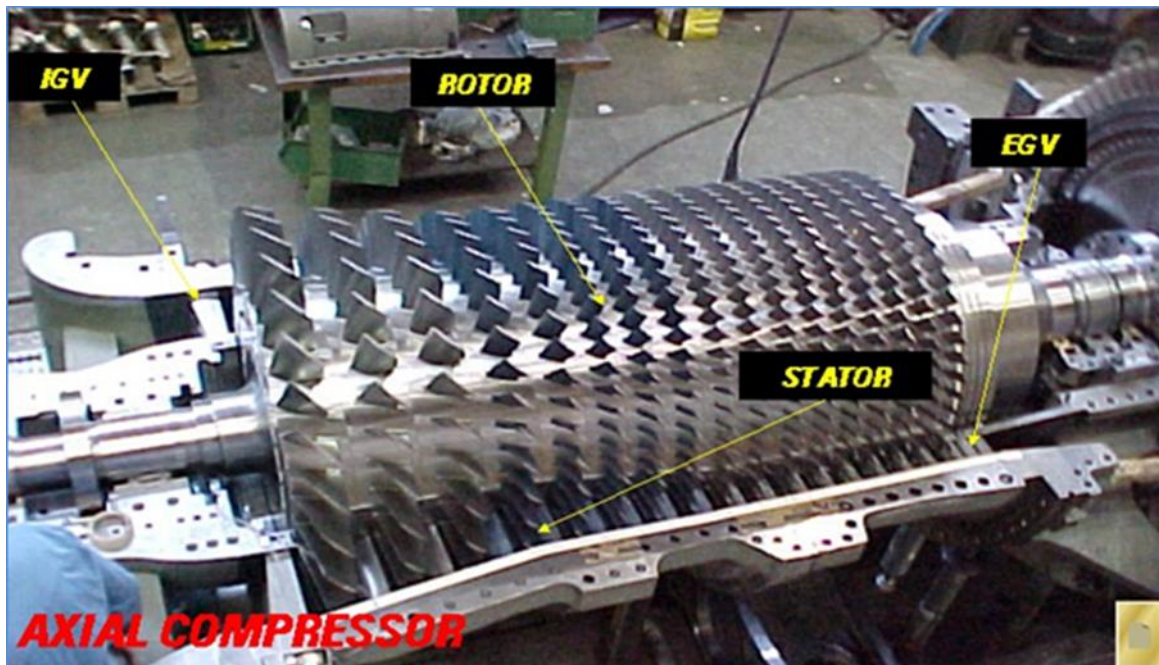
Carter du compresseur model 5002 et ensemble rotor de la turbine H.P [4].
